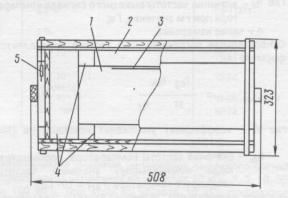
Схема упаковки прибора: 1 — укладочный ящик; 2 — влагозащитная бумага; 3 — полиэтиленовый чехол; 4 — подушка (гофрированный картон); 5 — пломба
